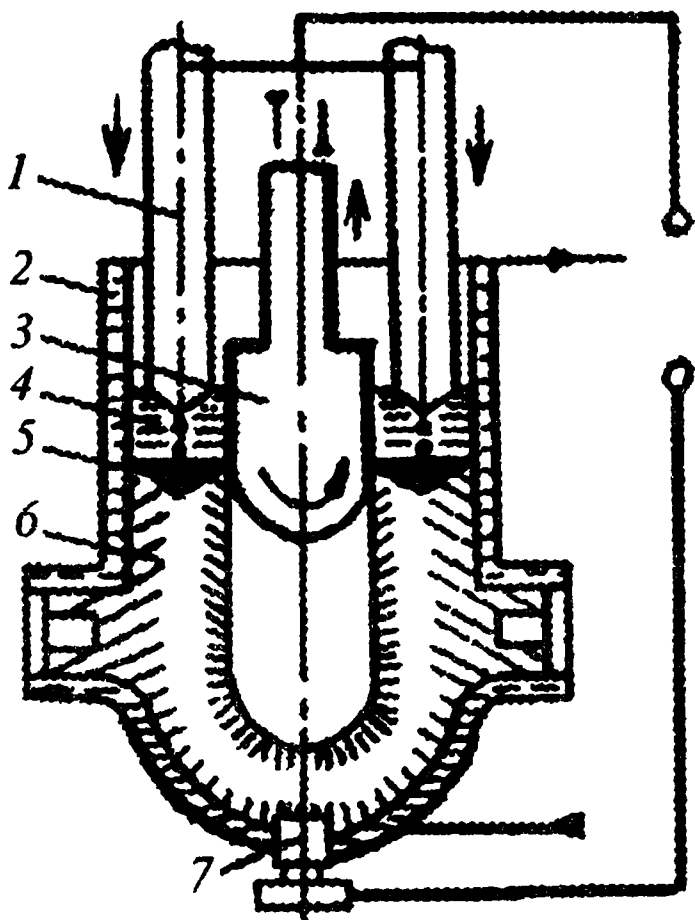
Получение отливки корпуса запорной арматуры способом ЭШЛ:
